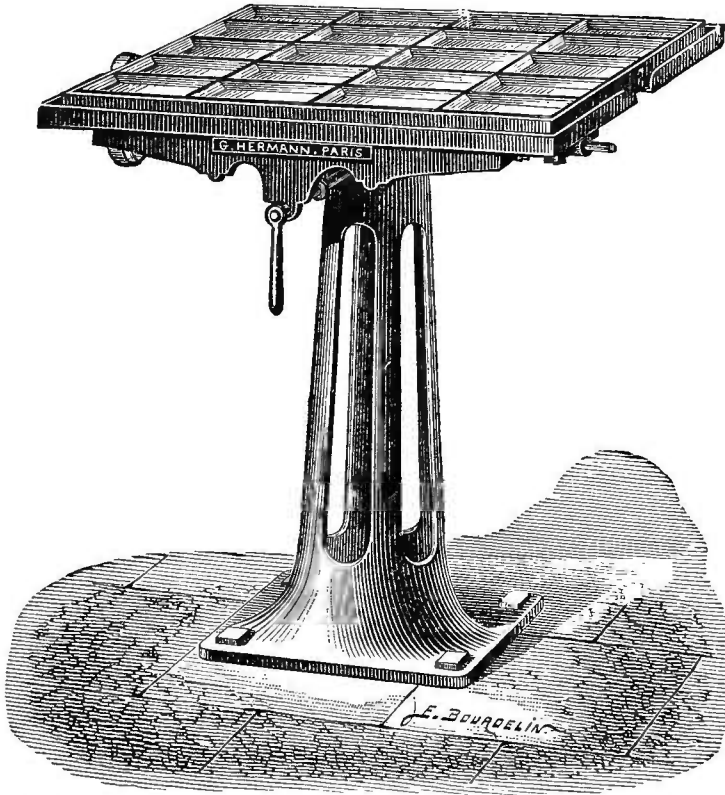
Machine à mouler les tablettes de chocolat, dite *tapoteuse*.
